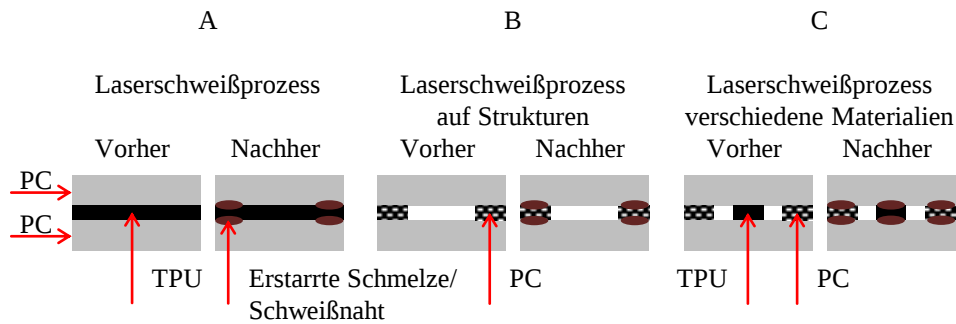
Schematische Darstellung vor und nach dem Laserschweißprozesses; A) Laserschweißprozess PC (transparent) zu TPU (absorbierend), flächige Schweißung; B) Laserschweißprozess PC zu PC, Schweißung auf Strukturen; C) Laserschweißprozess PC zu PC und TPU, Schweißung auf Strukturen.
